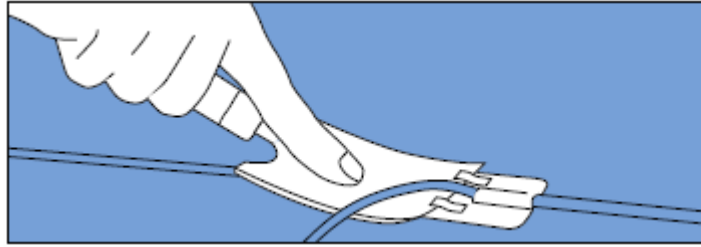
Aparar (reduzindo o cordão de soldadura com uma guia de nivelamento e espátula de corte)
